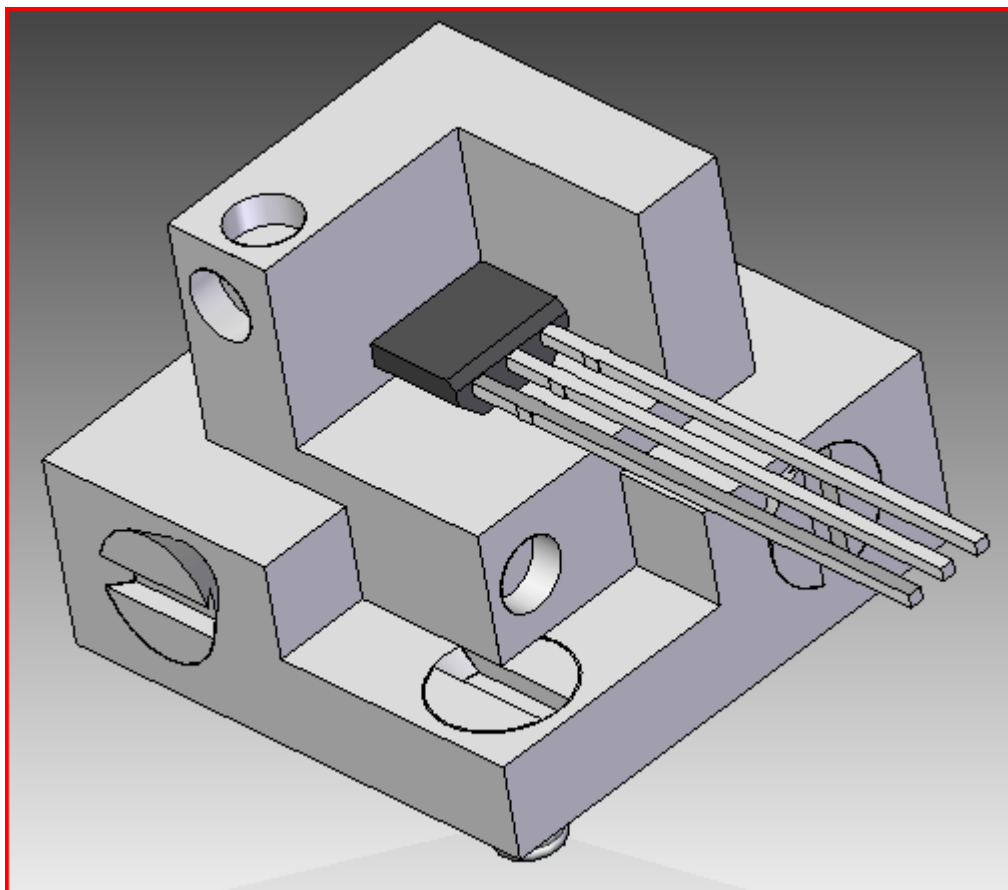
Diseño final en Solid Edge de cubo seccionado, posición 1
